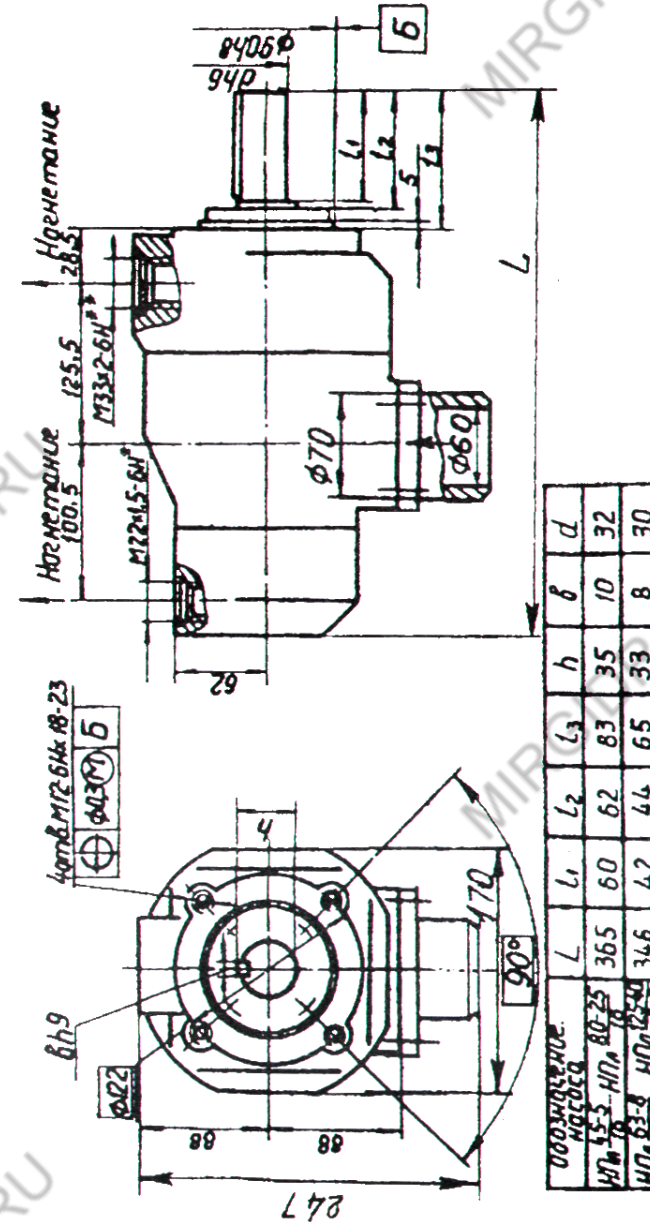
Габаритные и присоединительные размеры насосов
